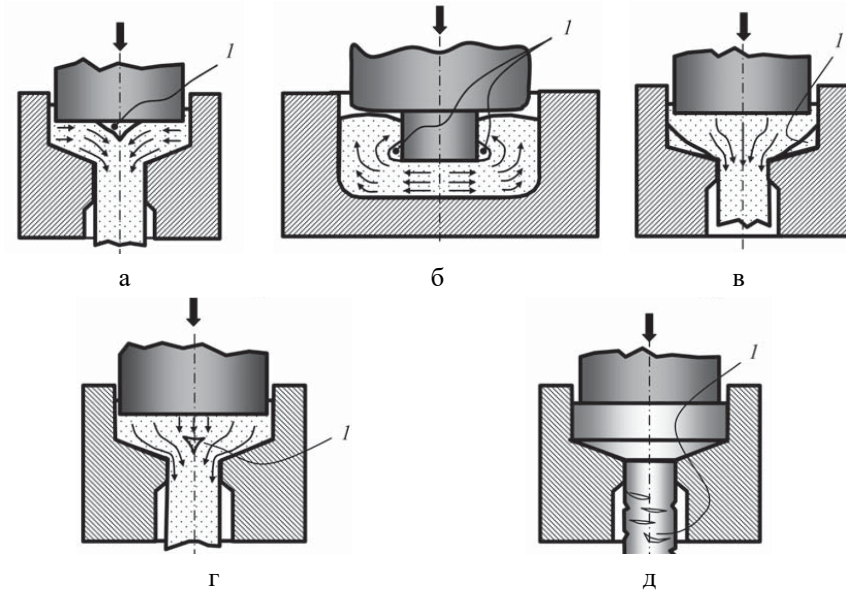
Схематичне зображення дефектів, що утворюються під час видавлювання: а – прес-утяжина; б – простріл; в – скол зовнішній; г – скол внутрішній; д – тріщини
